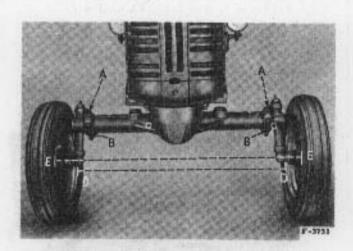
1 - Support de montage d'essieu avant. 2 - Axe de pivot d'essieu avant.
